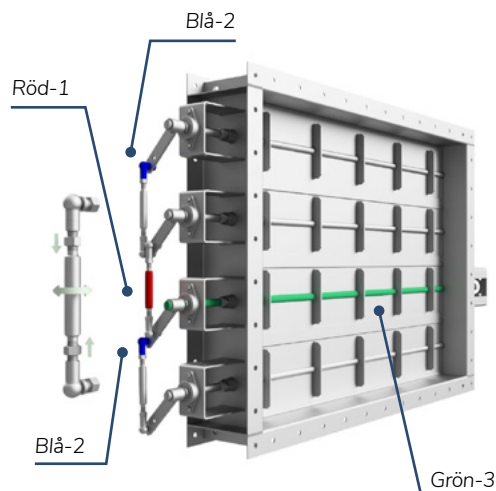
& 2 länkmarm, från vänster. Bild 1 visar låsmuttrar på länkarmen. Bild 2 visar exempel på drivaxel i grönt.
